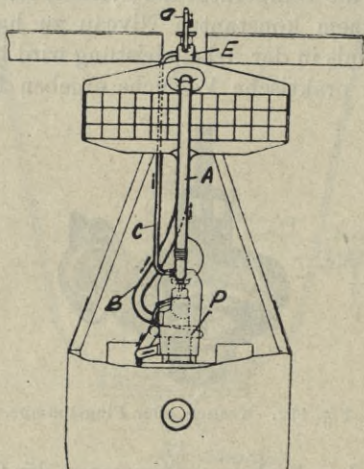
u. 113b. Kühlanlage mit Stirnkühler.
